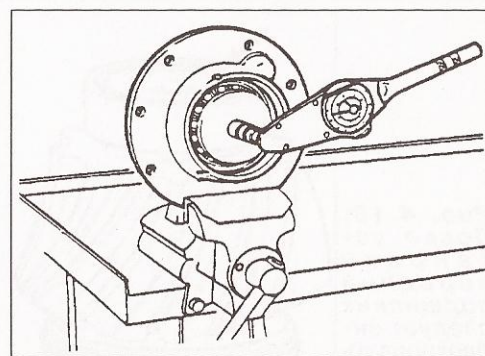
Проверка предварительного напряжения подшипников дифференциала.
